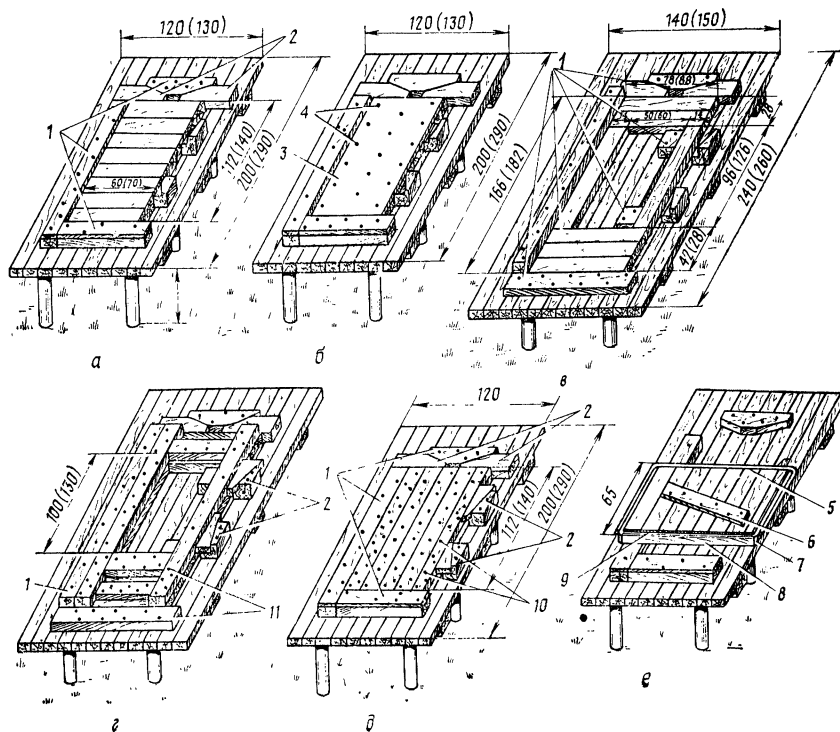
Сборка полотна и коробки дверного блока БД-50 (БД-60):
